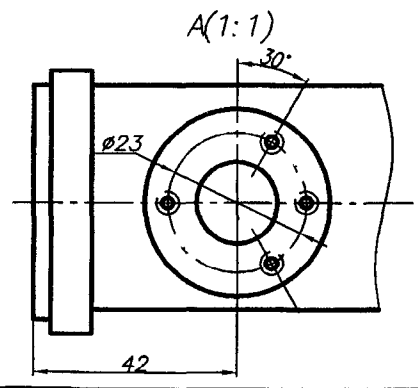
, б. Пример оформления сборочного чертежа сварной сборочной единицы
